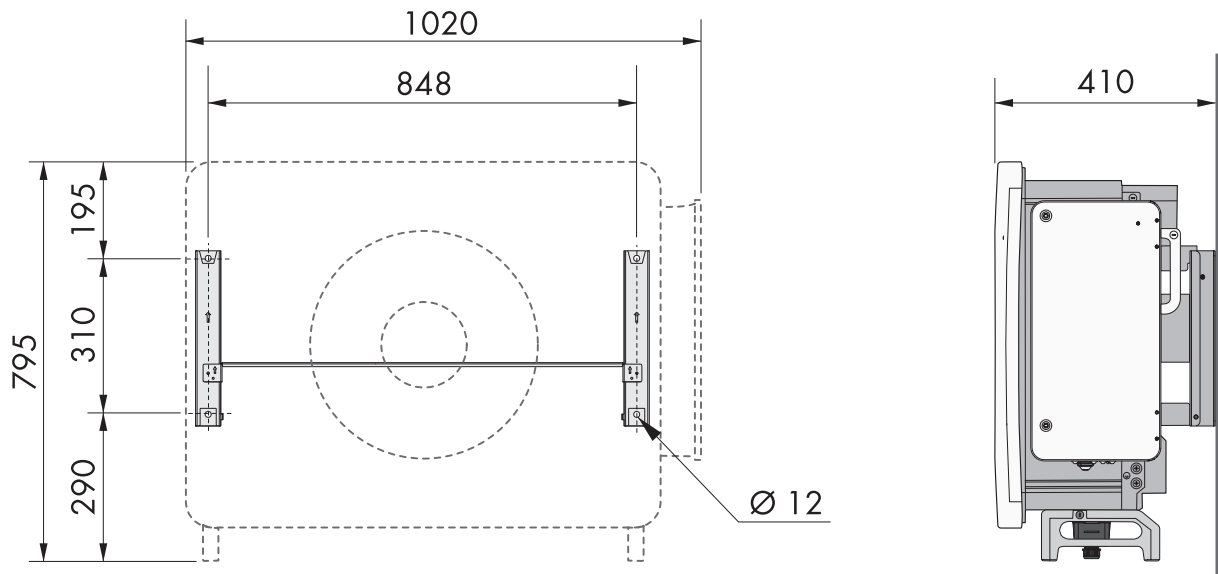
Dimensionado del soporte de montaje (medidas en mm)
